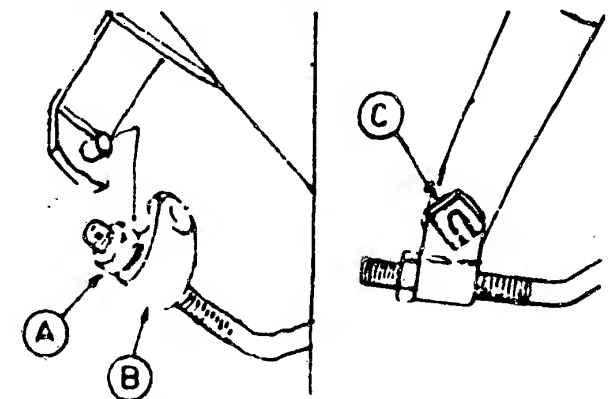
links: Zum Einstellen der Schaltstange am Automatikgetriebe ist die Kontermutter A zu lösen und das Endstück B zu verdrehen. rechts: Die Schaltstange ist auf beiden Seiten eingehängt und mit einem Clips gesichert.
